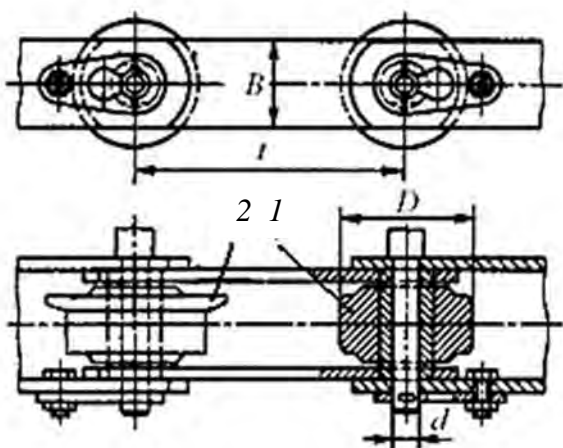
Пластинчатые цепи катковые: *1* – с гладкими катками; *2* – с ребрами на катках пластинчатой втулочной цепи
